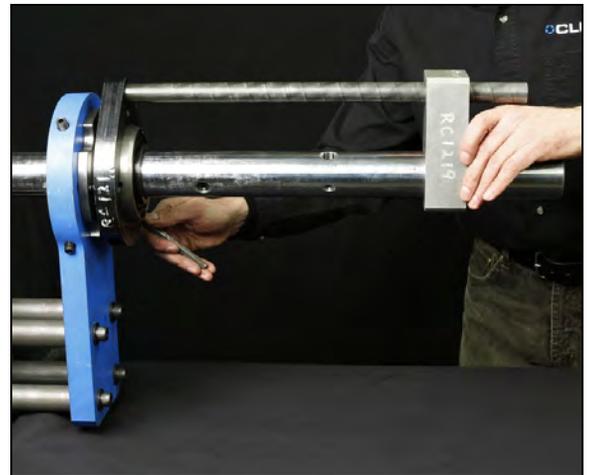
OUTIL D'ALIGNEMENT SUR LA TIGE DE MONTAGE
